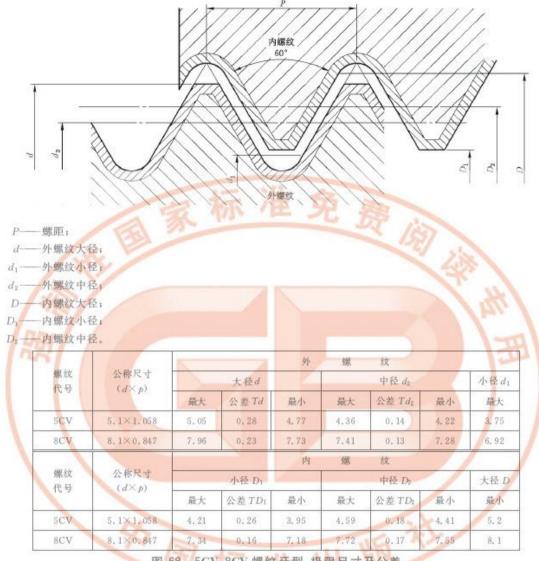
5CV、8CV 螺纹牙型、极限尺寸及公差
